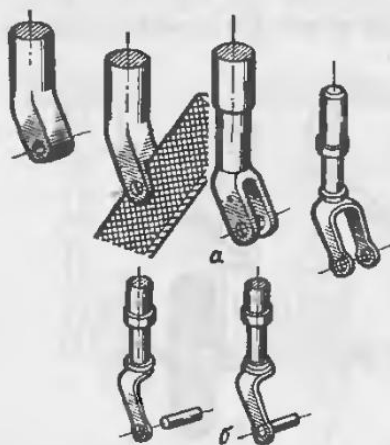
Изготовление цельной стойки шасси: а - виличатой; б - полувиличатой
